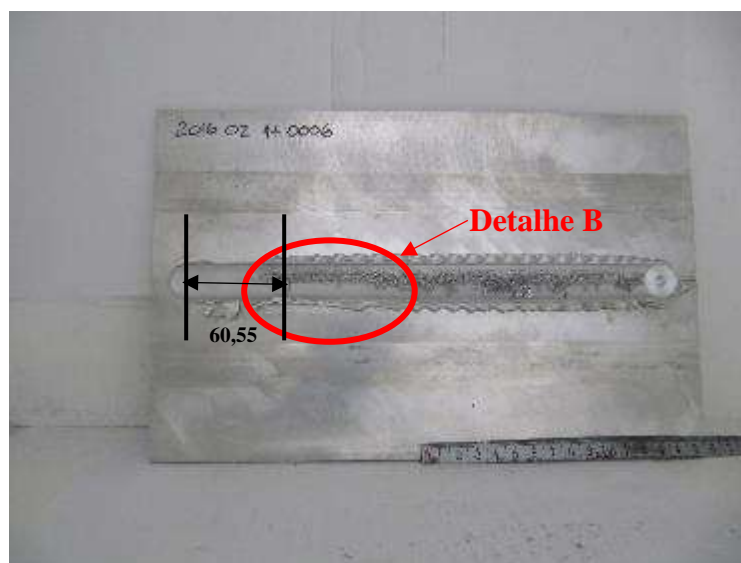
Junta de topo dissimilar soldada por FSW. Detalhe B indicando início de formação de rebarba excessiva.
